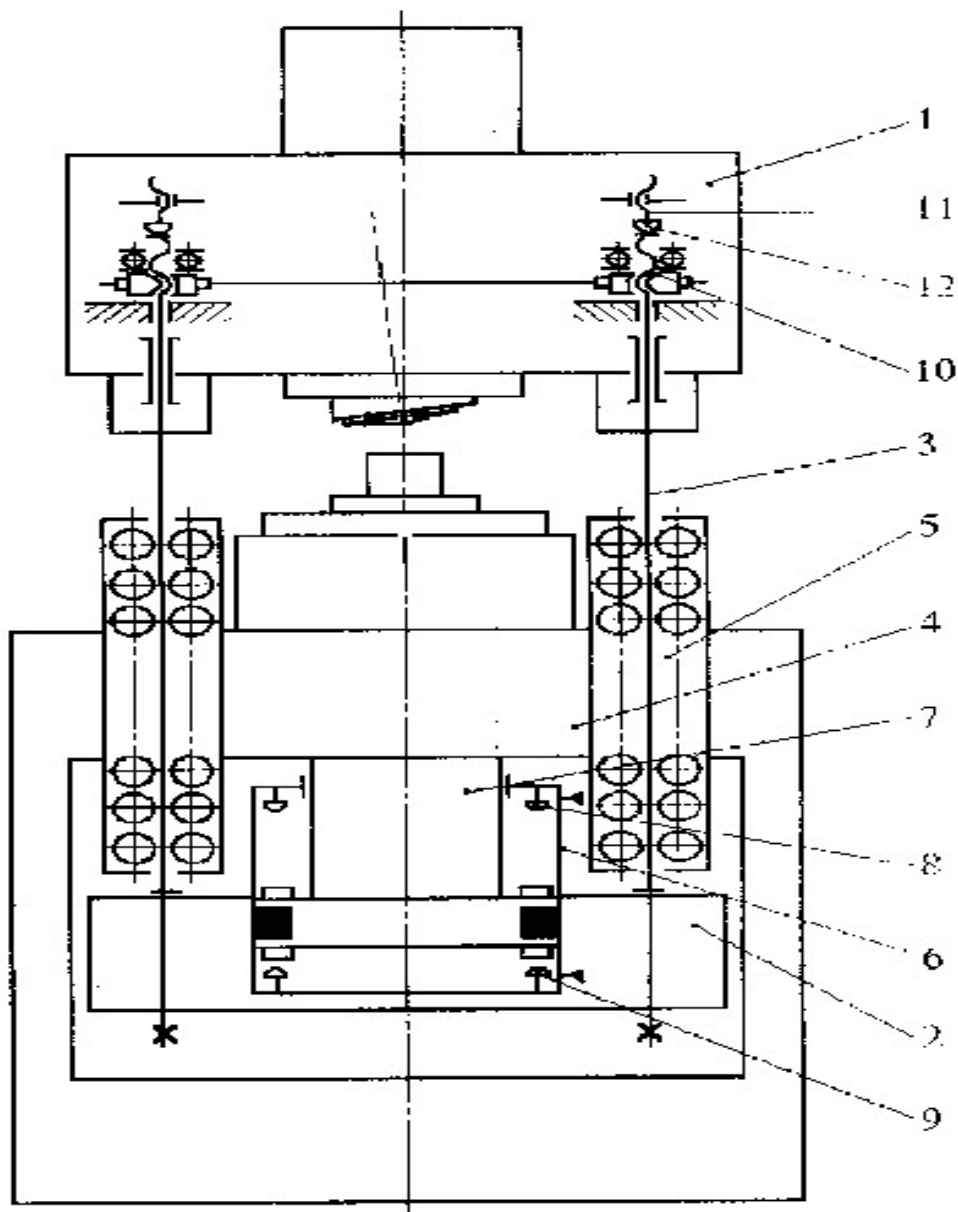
Конструктивна схема преса ПДШО – 280/30
